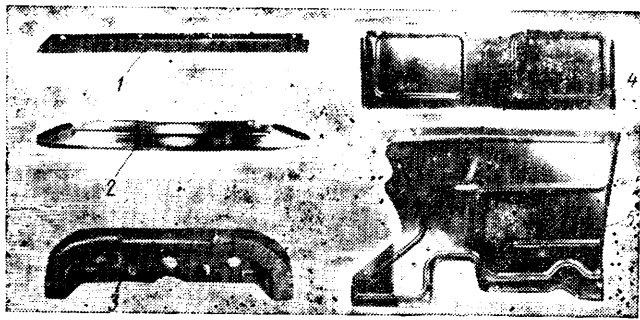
Детали, изготовленные из стали 08ГСЮТ:
